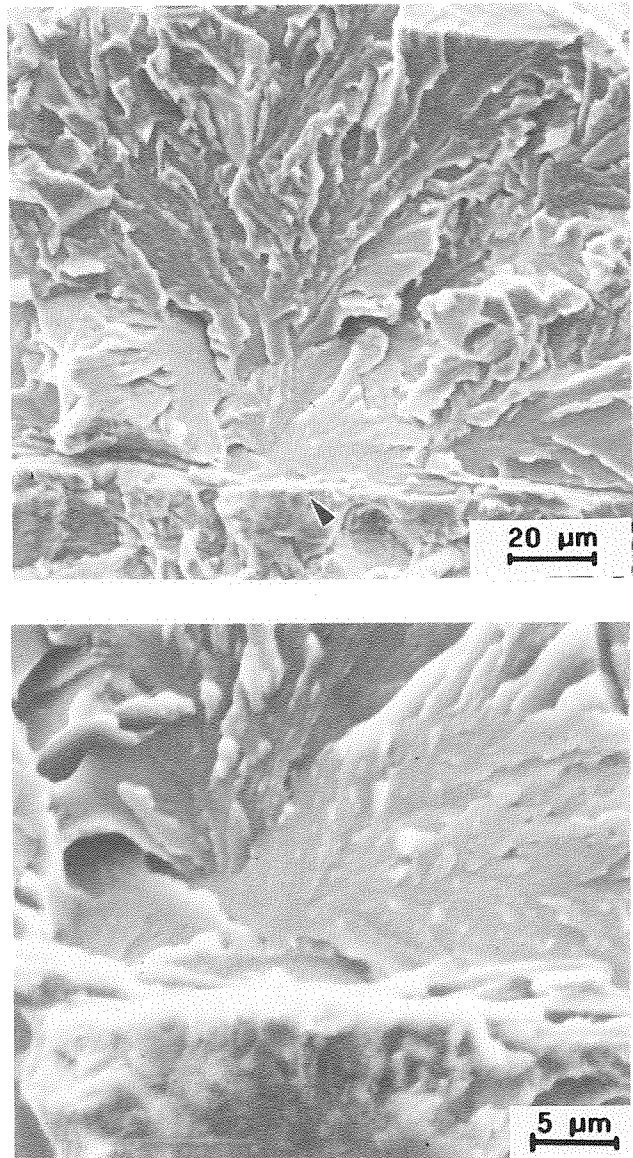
Estallido frágil originado a partir del borde de la grieta de fatiga.
